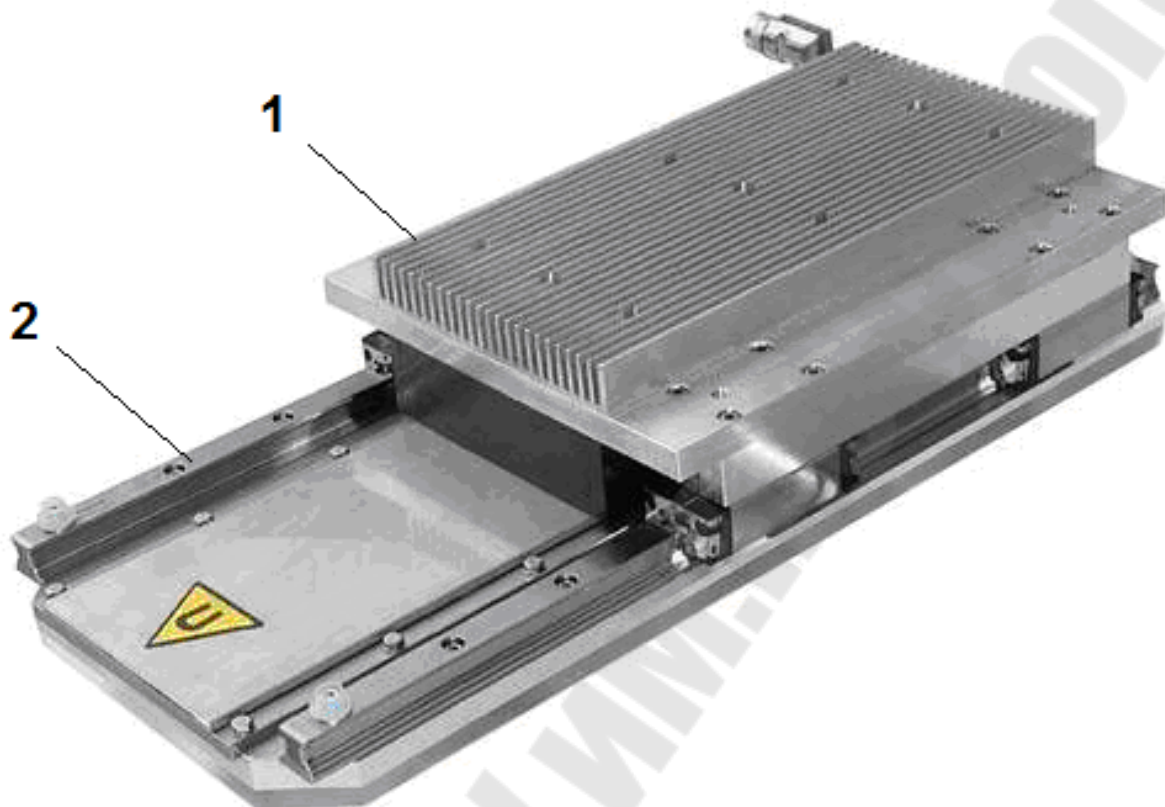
Мехатронный модуль с линейным двигателем
